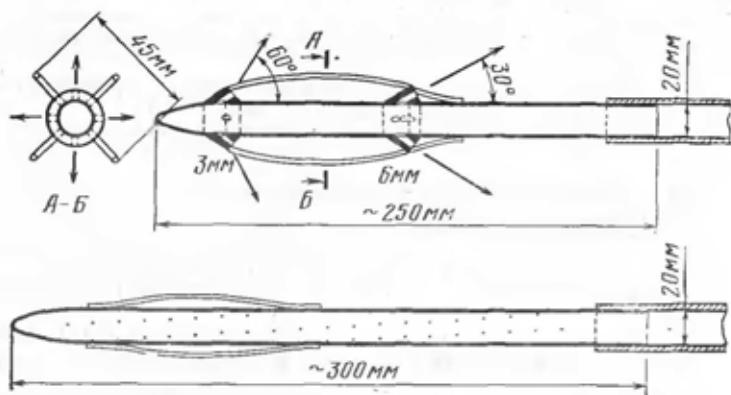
Чертеж струйчатой трубы промывного аппарата [10.2]: сверху — для промывки назад; внизу — для промывки в сторону (масштаб не соблюден); внутренний диаметр труб 20 мм.
